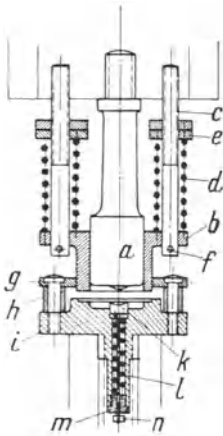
Ziehwerkzeuge zu Abb. 487 und 487a.
